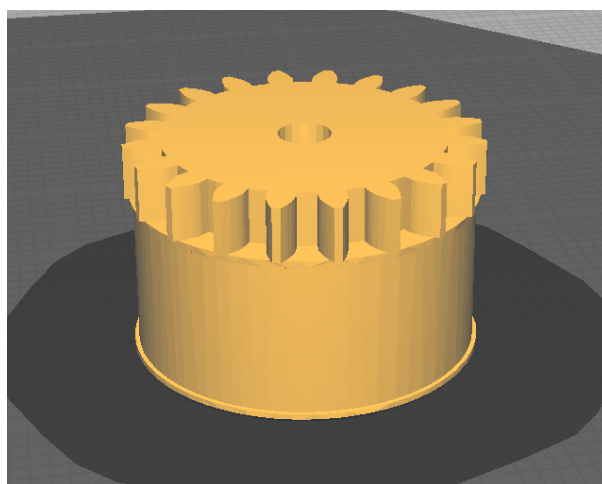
Par roda/engrenagem pronto para ser fabricado
